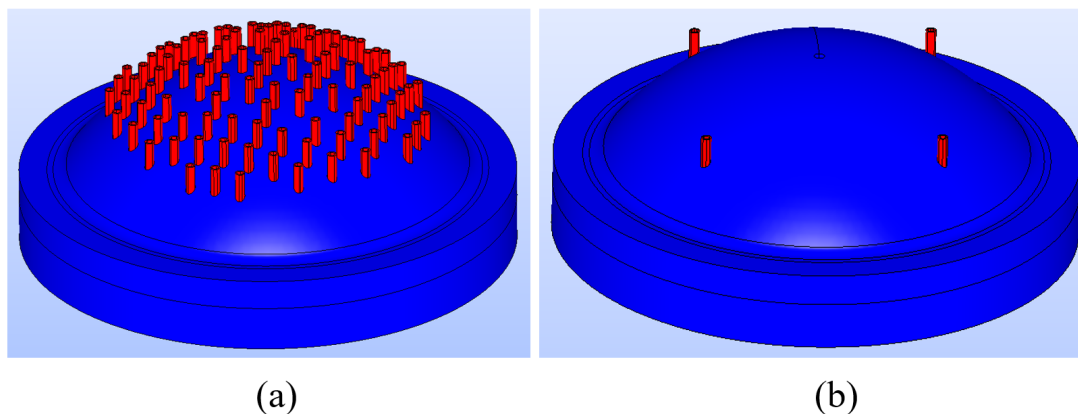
Couvercle de cuve (en bleu) avec les tubes adaptateurs (en rouge) : (a) Géométrie complète et (b) Configuration étudiée
